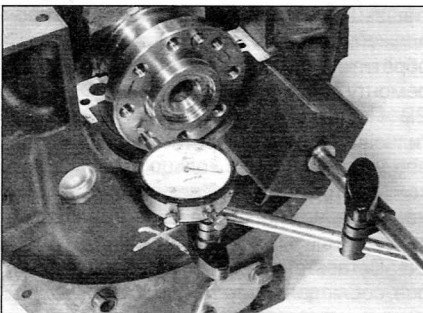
Осевой зазор коленчатого вала можно проверить с помощью стрелочного индикатора...
